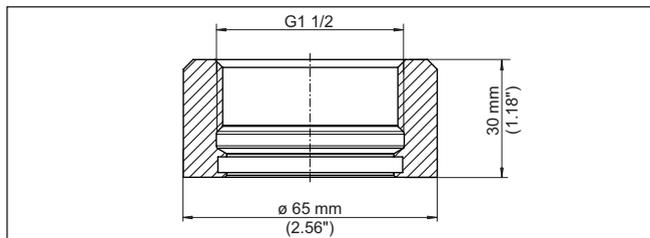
Medidas da luva para soldagem rosca G1 (ISO 228-1) - design higiênico
